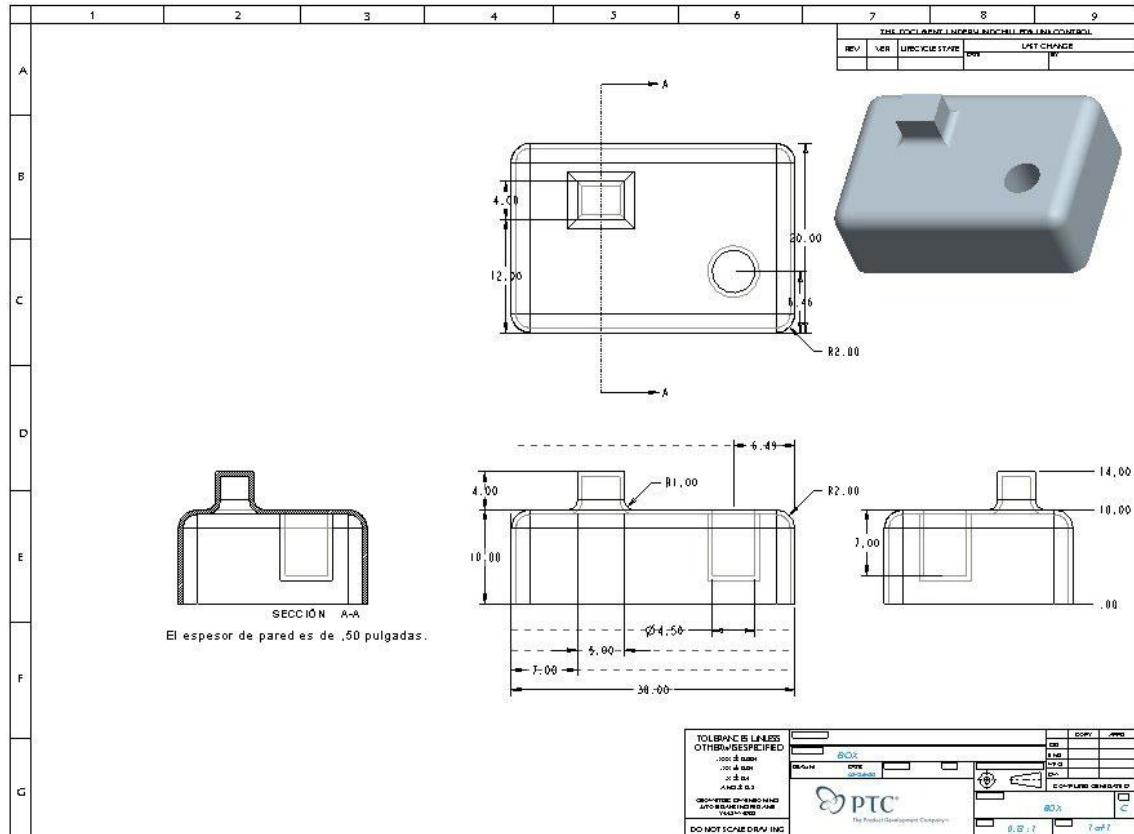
Plano en ProEngineer con cuatro vistas [18]
